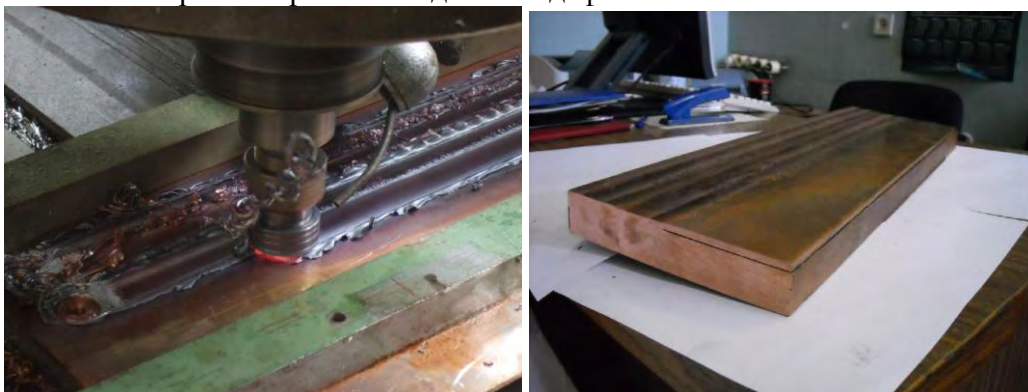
Фото: а – процесса наплавки; б – плиты кристаллизатора после частичной наплавки и порезки.
